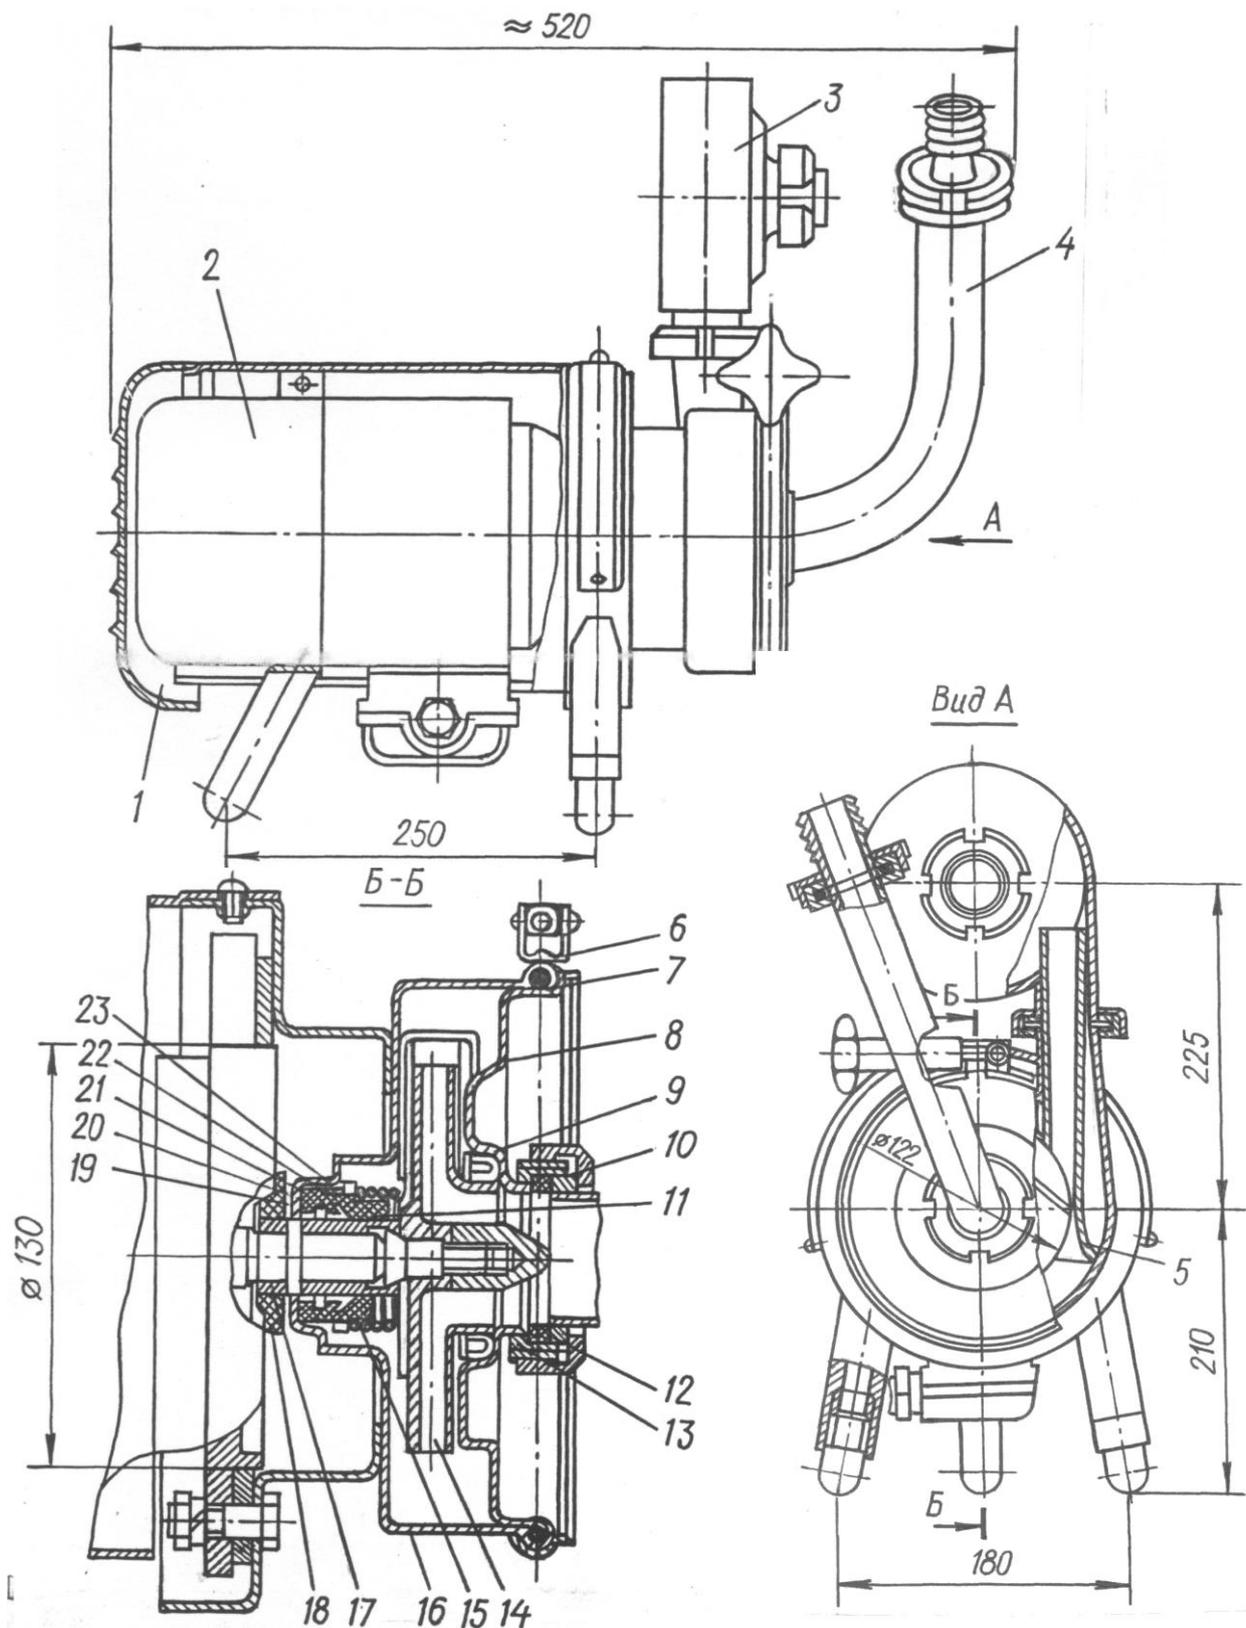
Общий вид электронасоса марки Е8-36-3Ц3,5-10: 1 – кожух; 2 – электродвигатель; 3 – воздухоотделитель; 4 – всасывающий патрубок; 5 – сопло; 6 – зажимное кольцо; 7, 20 – резиновые кольца; 8 – крышка; 9, 11 – манжеты; 10 – уплотнительное кольцо; 12 – накидная гайка; 13 – гайка; 14 – рабочее колесо; 15, 23 – пружины; 16 – корпус; 17 – наконечник; 18 – отражатель; 19 – неподвижное кольцо; 21 – подвижное кольцо; 22 – обойма
